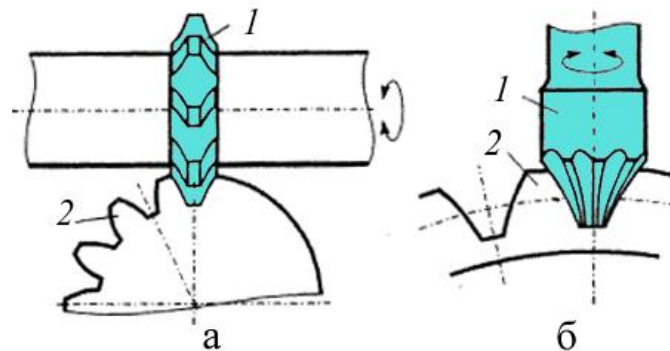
Схема нарізання зубчастих коліс методом копіювання: а – дисковою модульною фрезою, б) – пальцевою модульною фрезою
